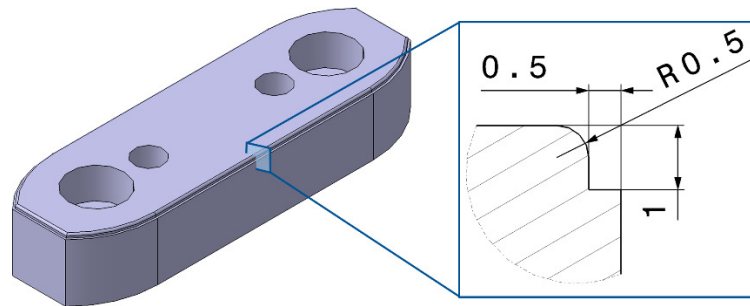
Gestufte Schneidkante am Stempel zur Reduzierung des Glattschnittanteils
